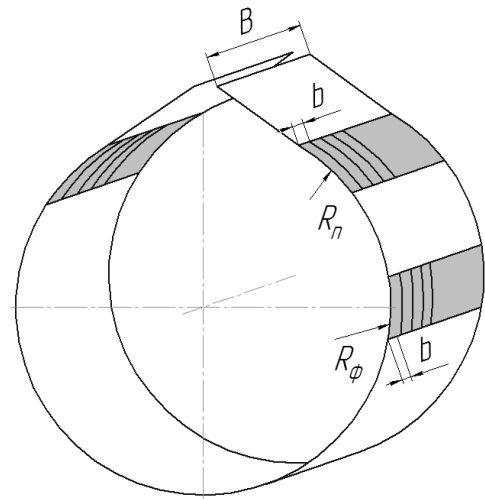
Схема вырезки образцов от кольца после формовки
